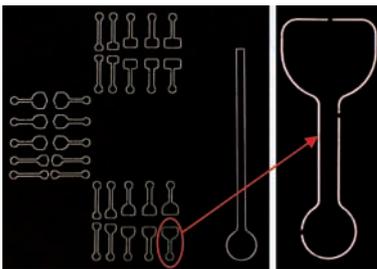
Laservorschnitt an Layout mit Detailausschnitt
